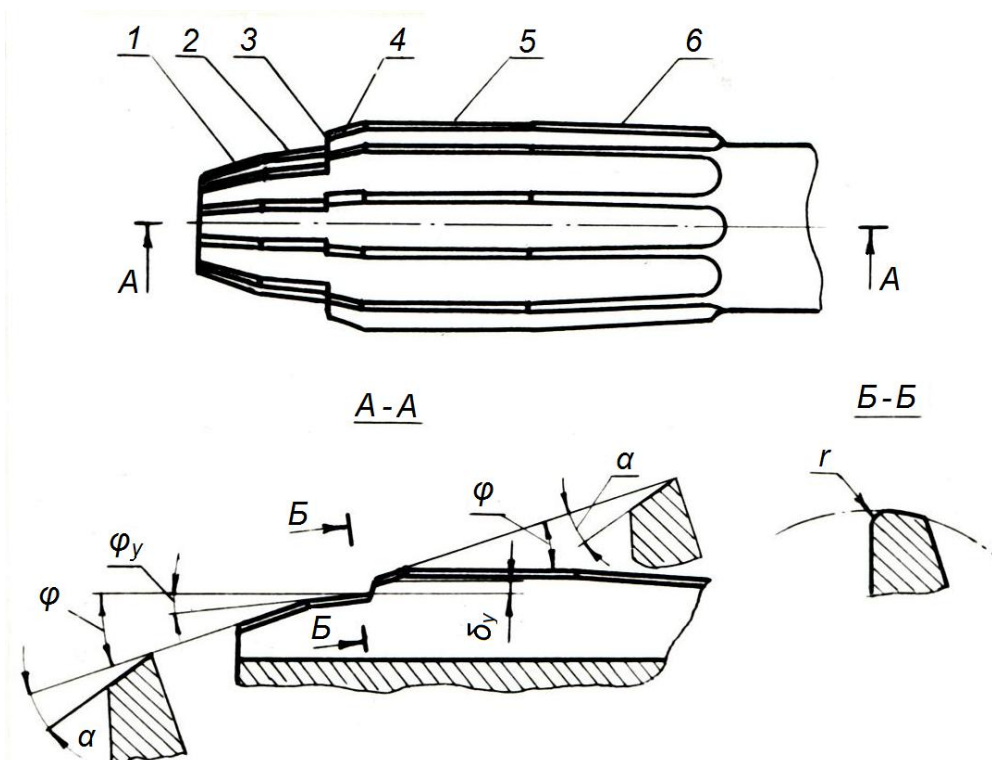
Конструкция режущей части развертки для резания с ОПД
